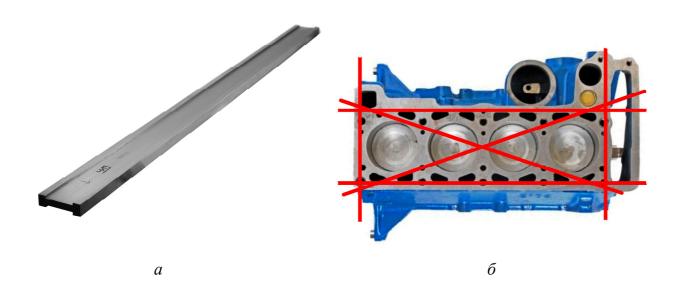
Проверка наличия коробления поверхности блока цилиндров: a — поверочная инструментальная линейка; δ — схема проверки плоскостности головки блока цилиндров
